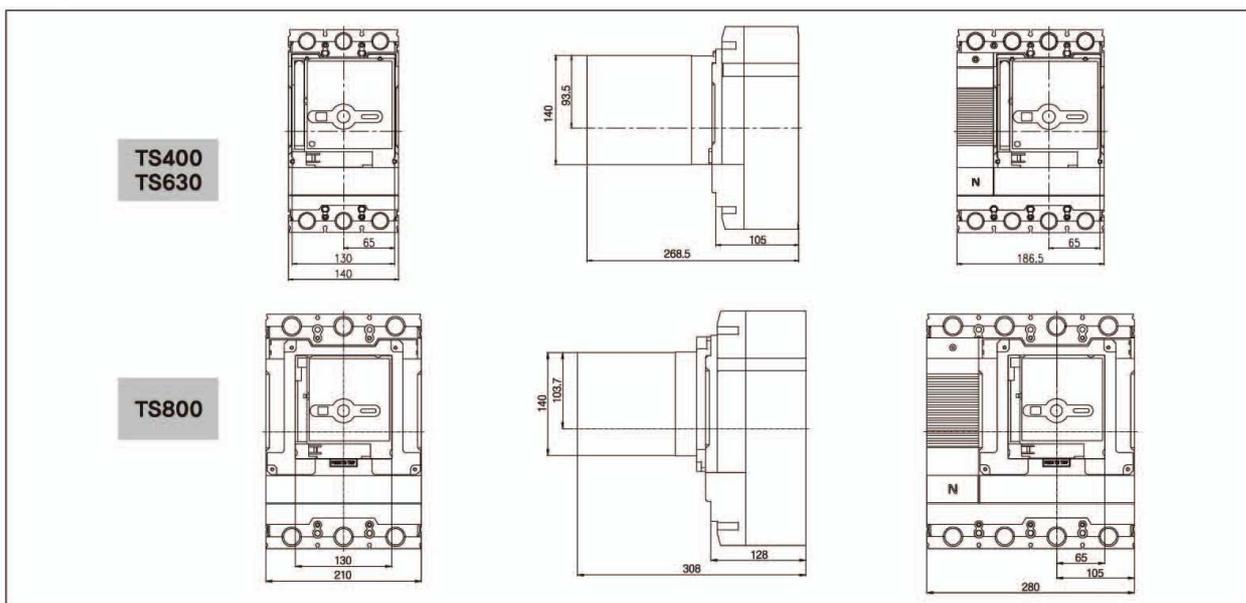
Габаритные размеры моторных приводов на выключатели TS400, TS630 и TS800
